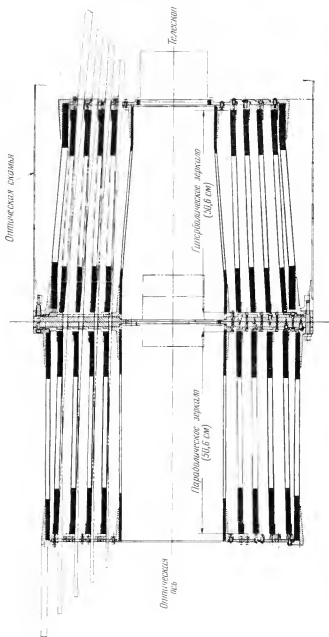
Механическая конструкция зеркала. Восемь зеркал из плавленного кварца крепятся инварными фланцами; крайние фланцы укреплены на графито-эпоксидных цилиндрах. Узел зеркала крепится за центральную инварную пластину.
